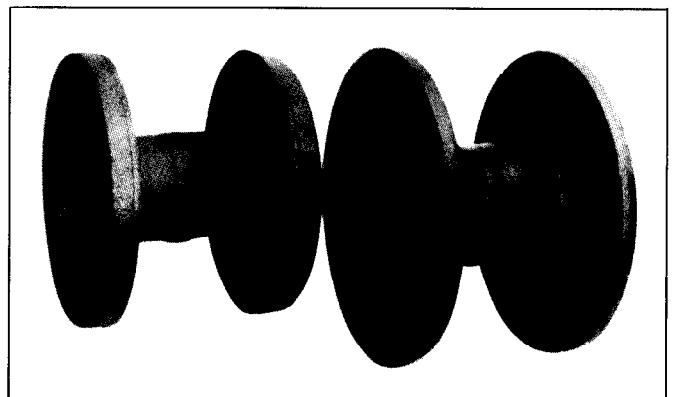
Schutzgasschweißen: Spulenkörper für Drahtcord (Baureihe mit Flanschdurchmesser von 100 bis 200 mm) aus C 35 V, Schweißquerschnitt von 750 bis 3500 mm²
